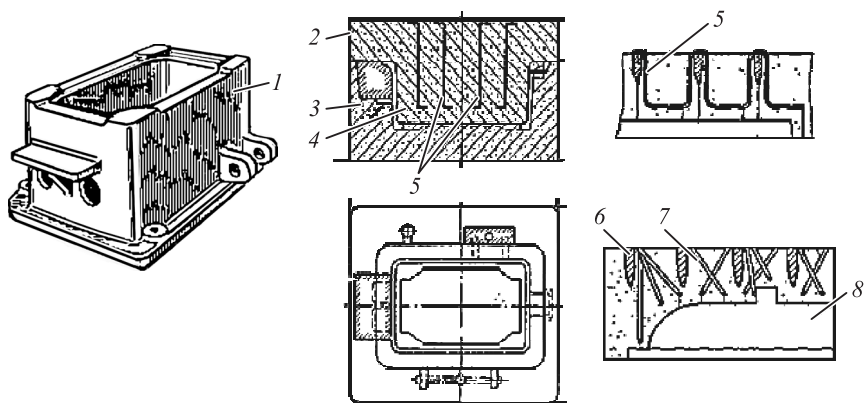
Элементы формы с песчаным болваном: 1 – отливка; 2 – верхняя полуформа; 3 – нижняя полуформа; 4 – песчаный болван; 5 – крючки; 6 – крестовина опоки; 7 – колышки (солдатики); 8 – модель
